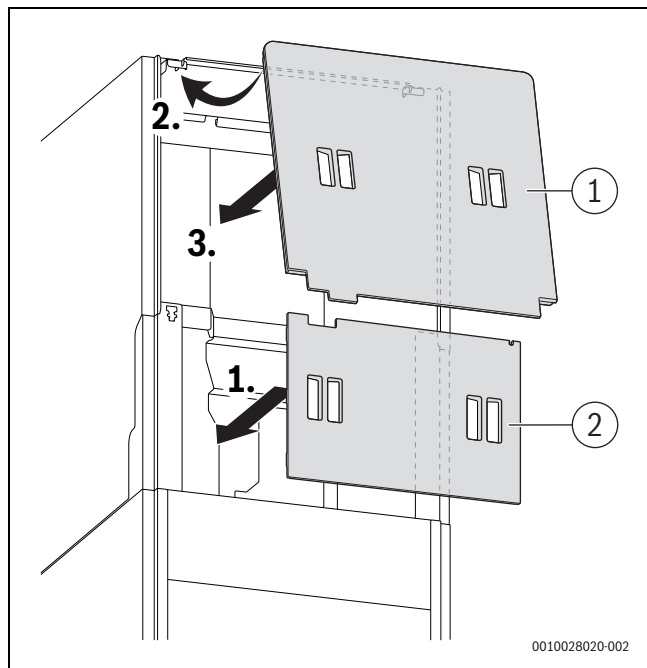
Установка теплоизоляции с обратной стороны (дополнительное оборудование SF 13)
